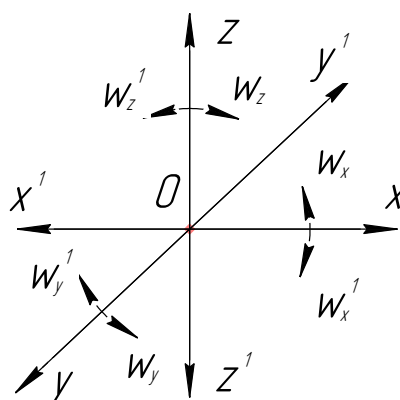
Схема одnobічних зв'язків, що покладають на заготовку
